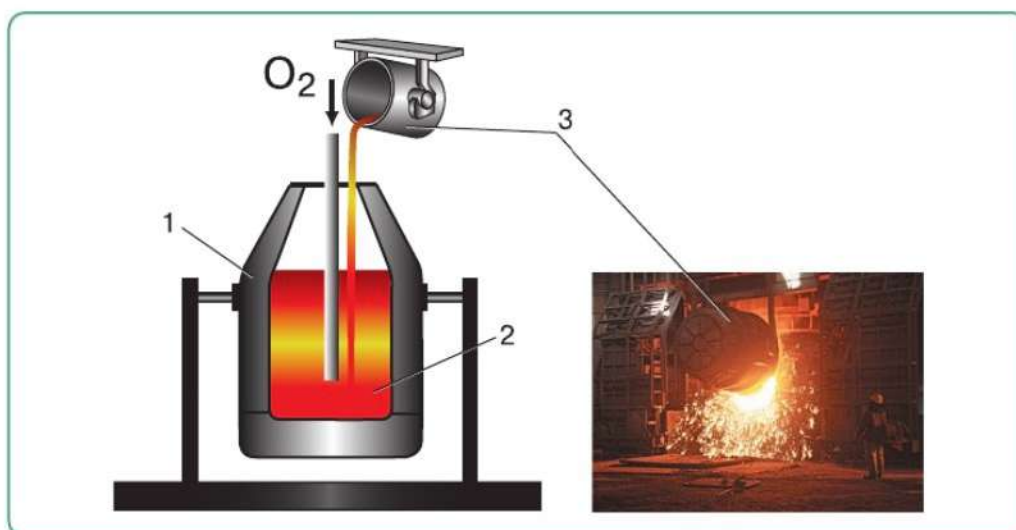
Схема устройства кислородного конвертора: 1 — корпус; 2 — сталь; 3 — ковш
